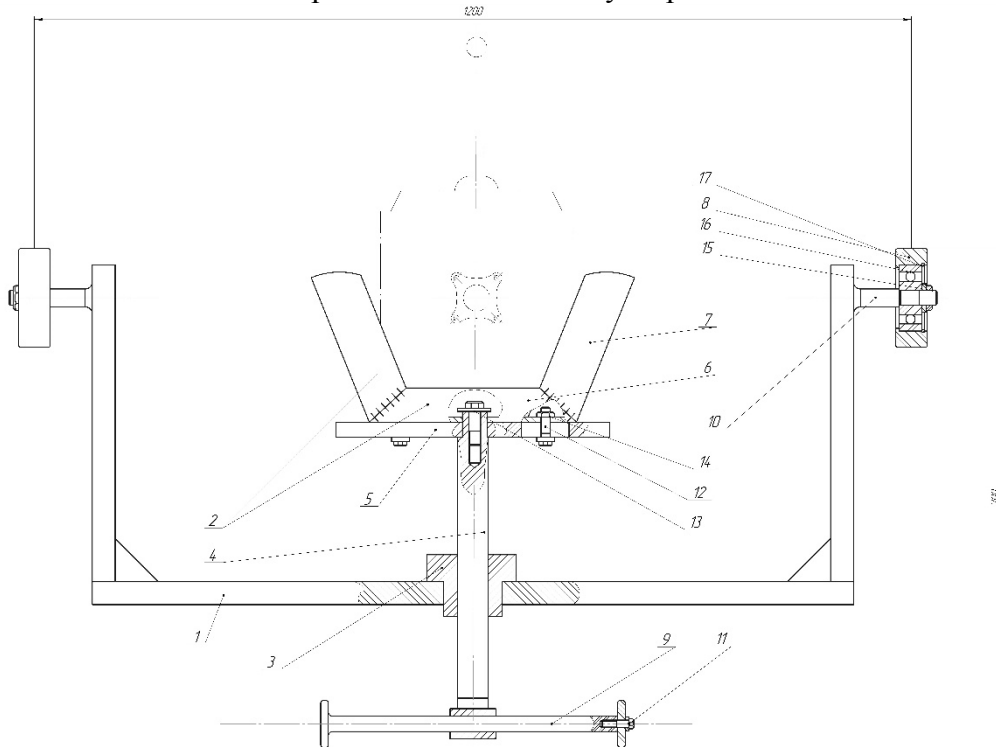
Пересувний візок для зняття і встановлення коробки передач
